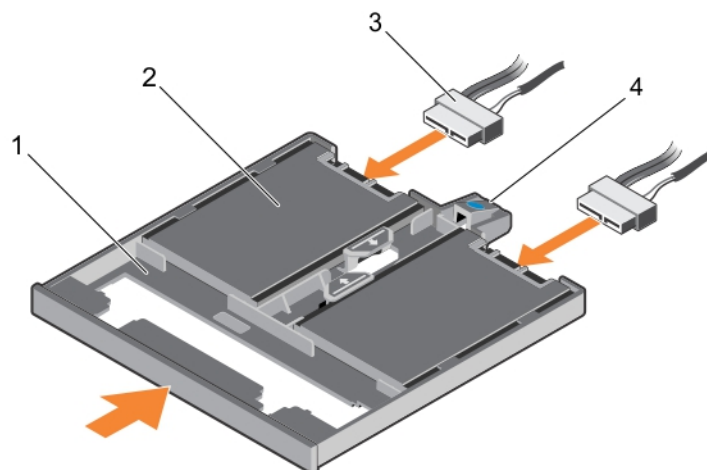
Instalación de la bandeja para SSD de 1.8 pulgadas
